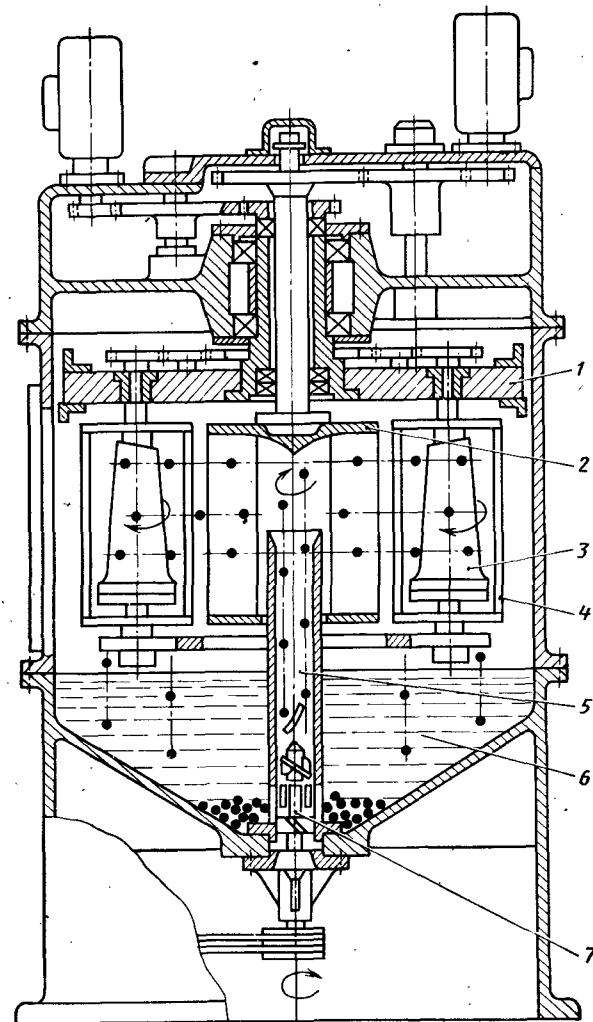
Схема виброгалтовки рабочих лопаток компрессора на установке ГРП-300: 1 — ротор; 2 — дробеметное колесо; 3 — обрабатываемая лопатка; 4 — кассета; 5 — направляющий аппарат; 6 — рабочая среда; 7 — осевой насос
